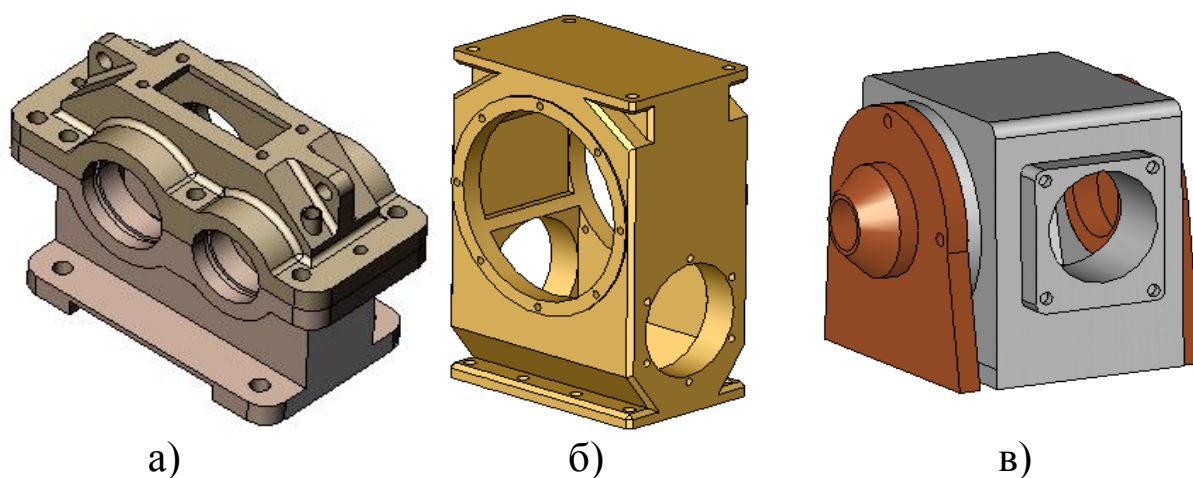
Корпуса редукторов: а – цилиндрический редуктор; б – червячный редуктор; в – конический редуктор
